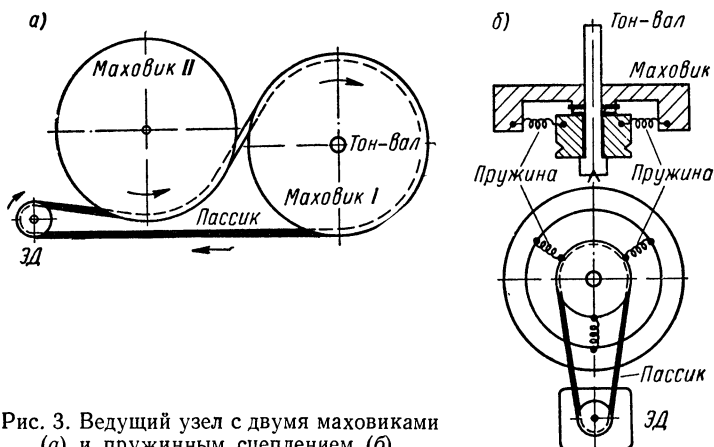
Ведущий узел с двумя маховиками (а) и пружинным сцеплением (б).
